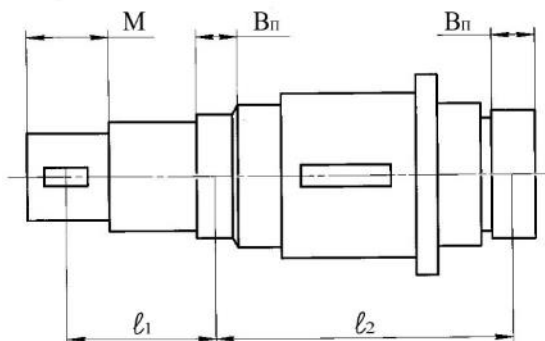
Вхідний вал одноступінчастого циліндричного редуктора
